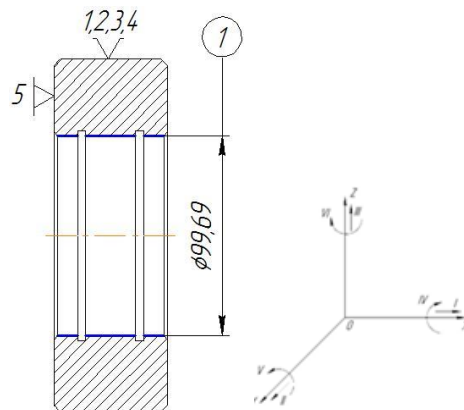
Схема базування заготовки на горизонтально-протяжній операції
